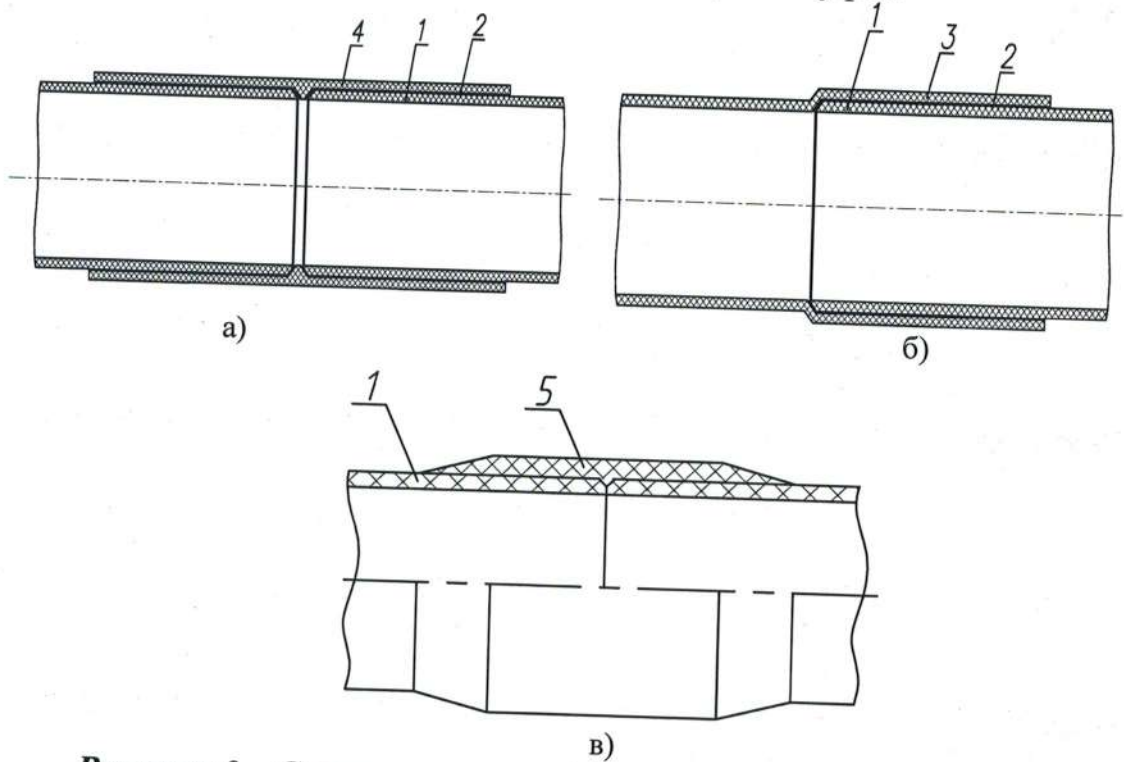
Схемы соединений стеклопластиковых труб на клею
